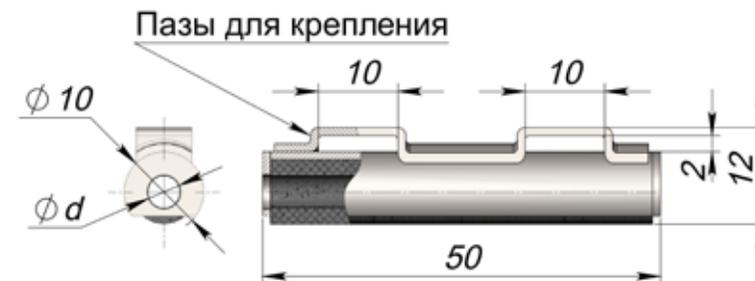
Габаритные и присоединительные размеры гильзы поверхностной.
